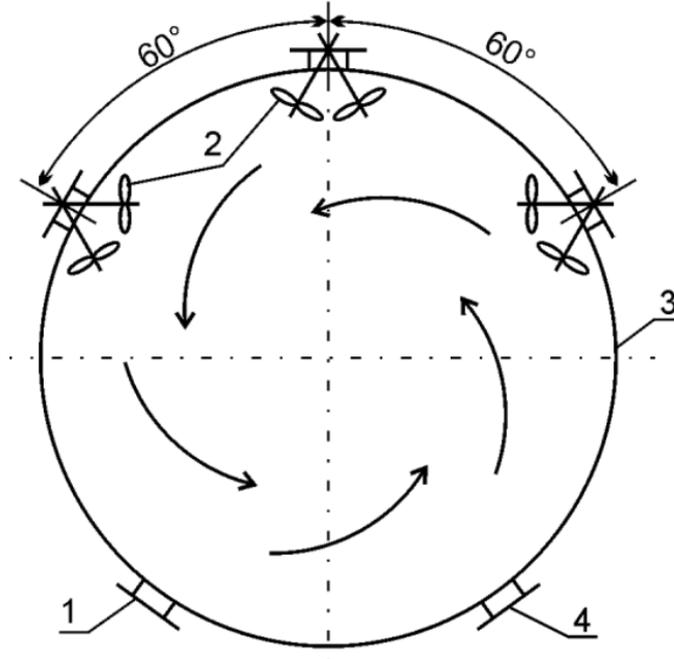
Схема установки в резервуаре винтовых смесителей: 1 – наливной патрубок; 2 – винтовой смеситель; 3 – стенка резервуара; 4 – сливной патрубок.
